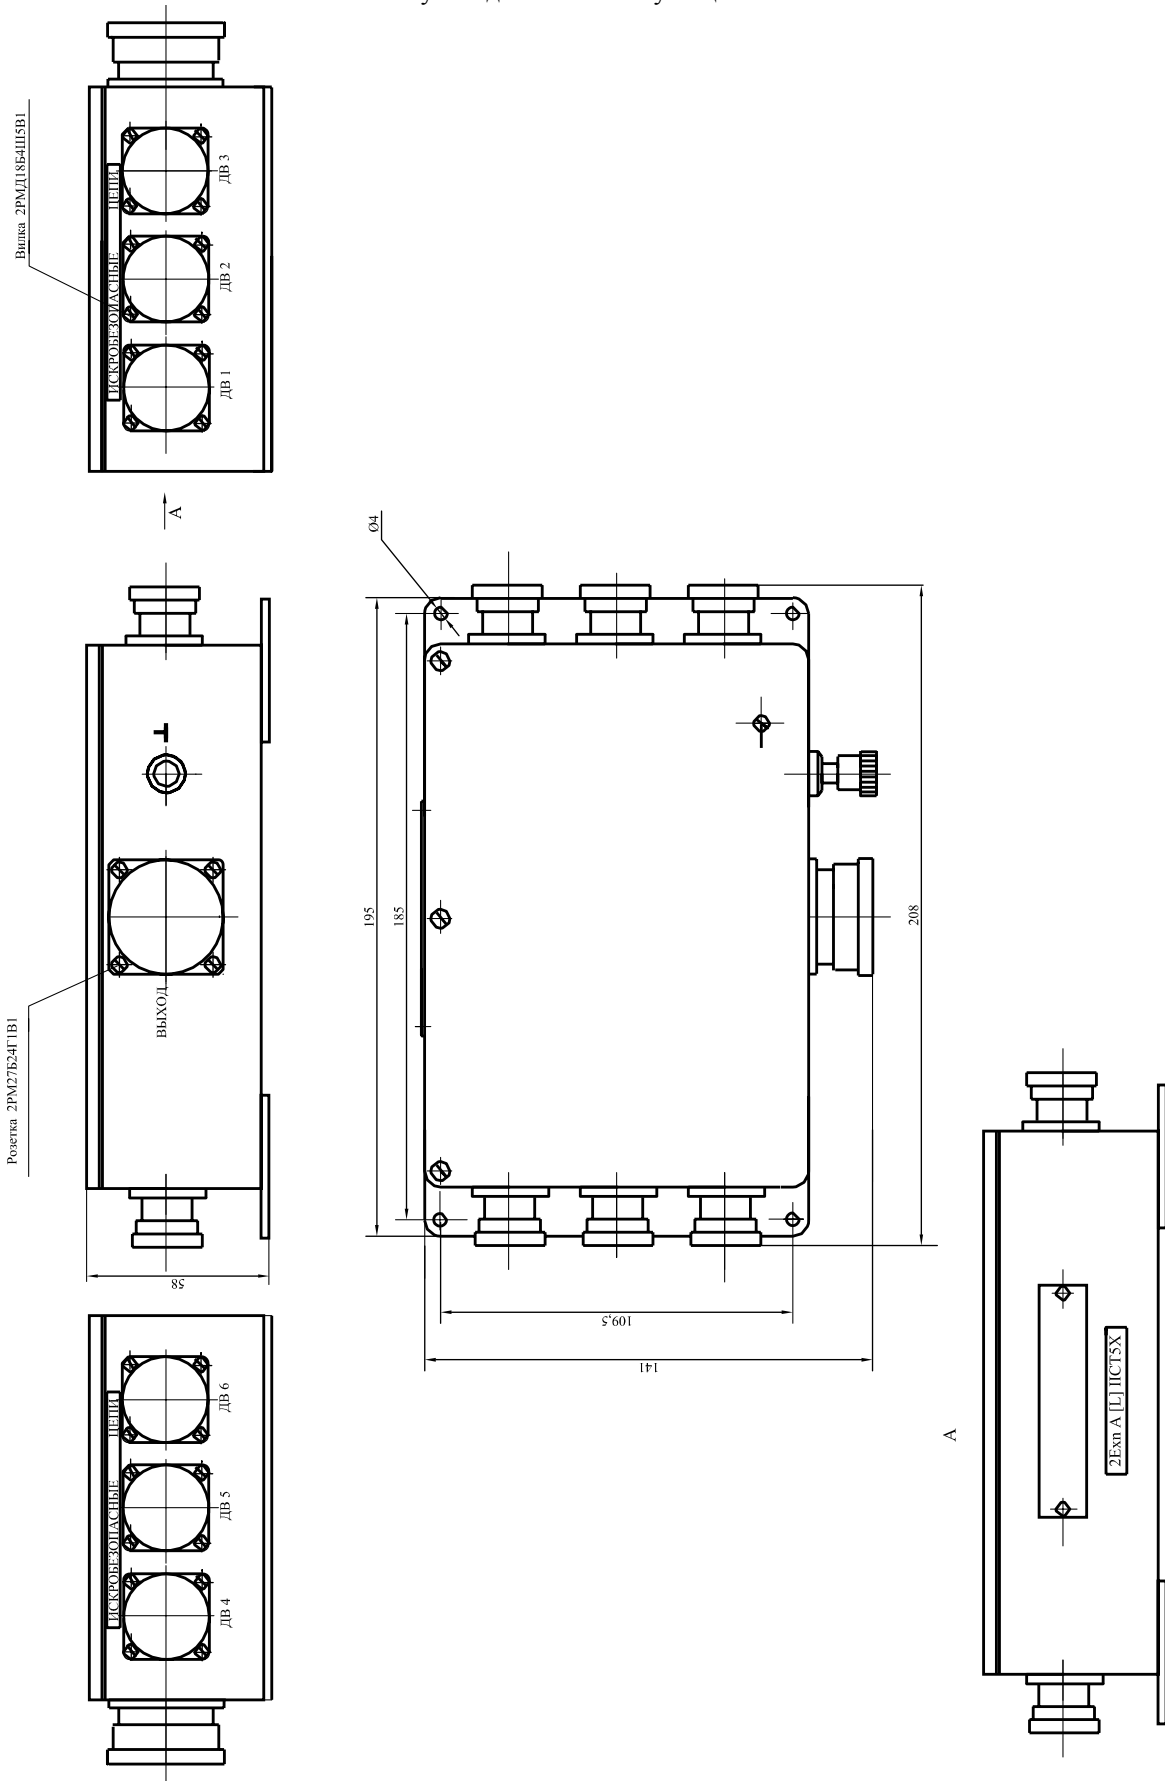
Габаритно-установочные размеры блока согласующего БС-16-45-6
